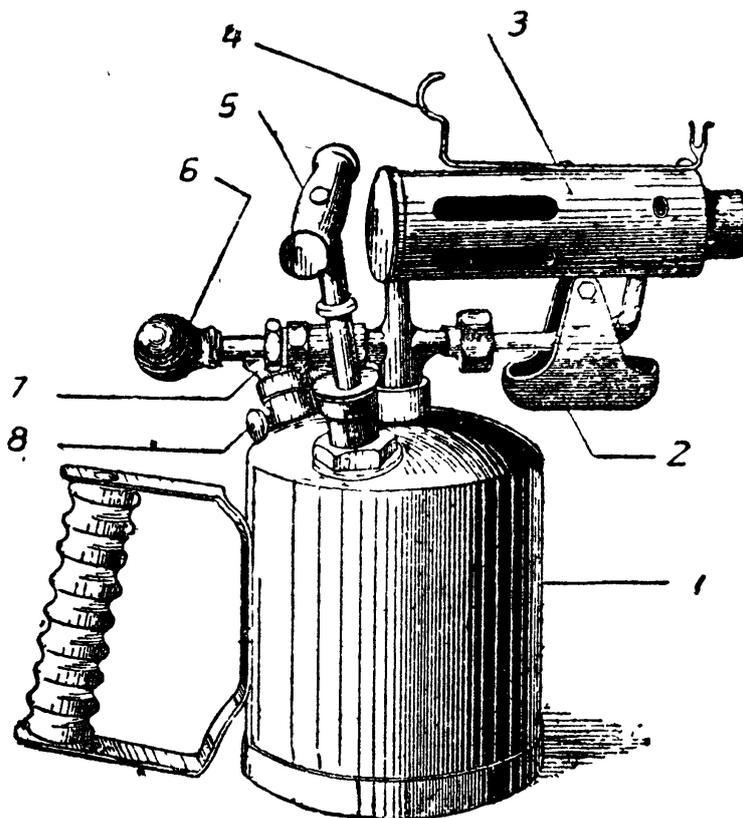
Паяльная лампа: 1—резервуар; 2—подогреватель; 3—горелка; 4—подставка для паяльника; 5—насос; 6—регулятор пламени; 7—пробка, закрывающая отверстие для наливания горючего; 8—винт для выпуска воздуха из резервуара
